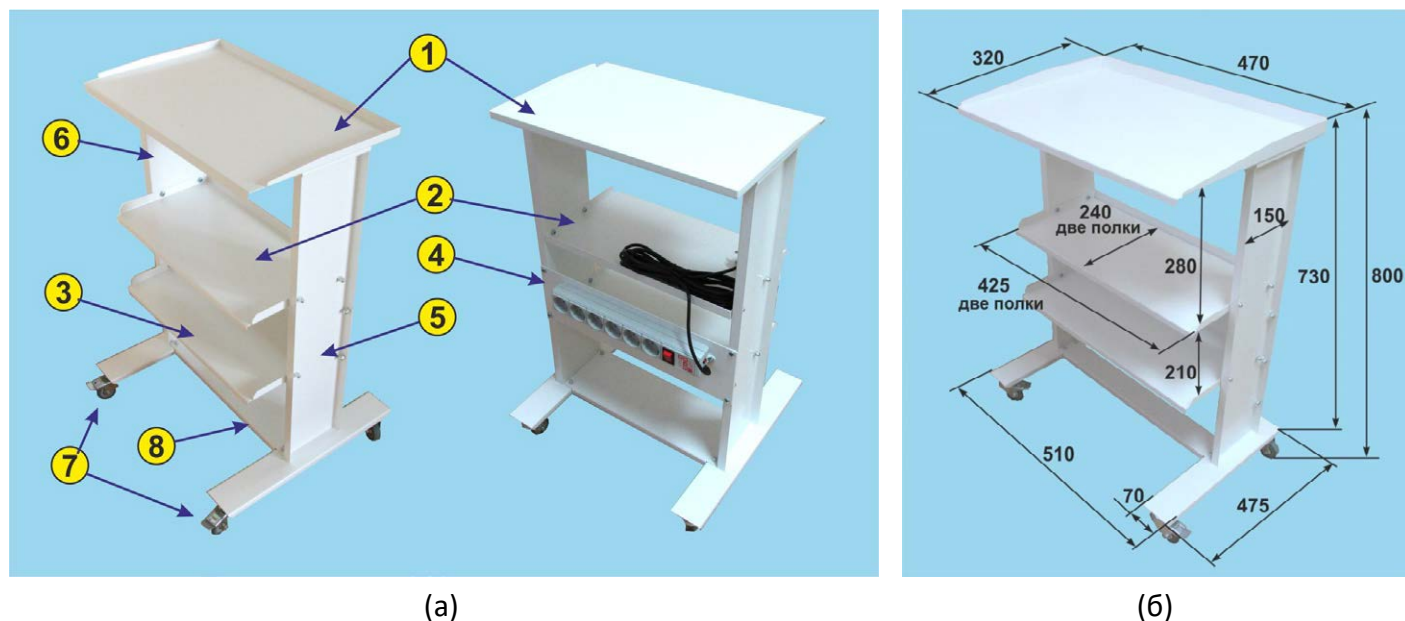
Внешний вид столика (а) и его габаритные размеры (б).
